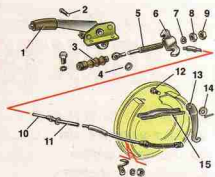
Детали стояночной тормозной системы: 1 – рычаг привода стояночного тормоза в сборе с кронштейном; 2 – ось тяги; 3 – защитный чехол; 4 – стопорная скоба; 5 – тяга; 6 – уравниватель троса; 7 – шайба; 8 – регулировочная гайка; 9 – контргайка; 10 – трос; 11 – оболочка троса; 12 – ось рычага; 13 – рычаг ручного привода колодок; 14 – шайба; 15 – разжимная планка колодок
